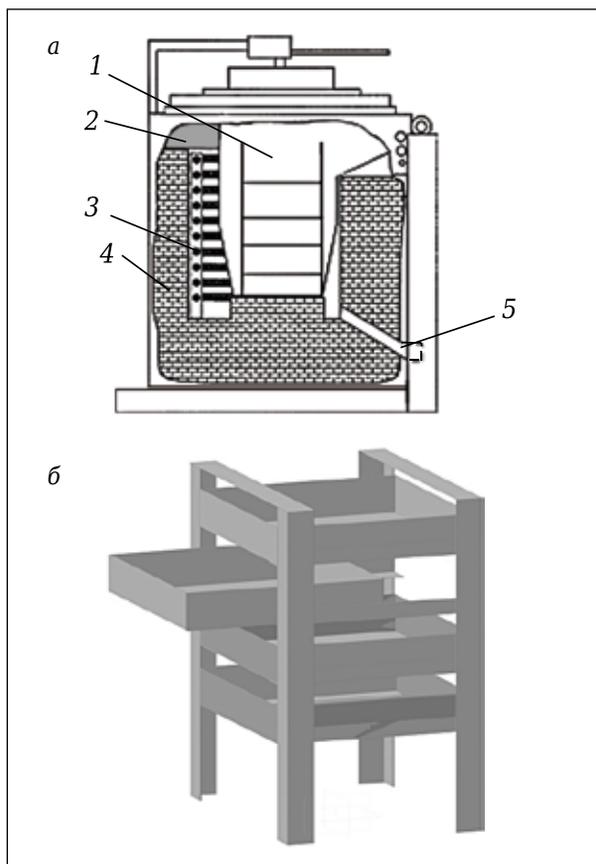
Электрическая печь косвенного нагрева (а) и агрегат для обжига (б): 1 — агрегат для обжига; 2 — верхняя теплоизоляция печи; 3 — нагреватели; 4 — футеровка; 5 — аварийный слив
